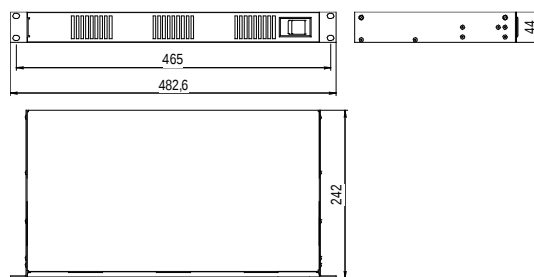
Габаритный чертеж ЩРЗ-7
